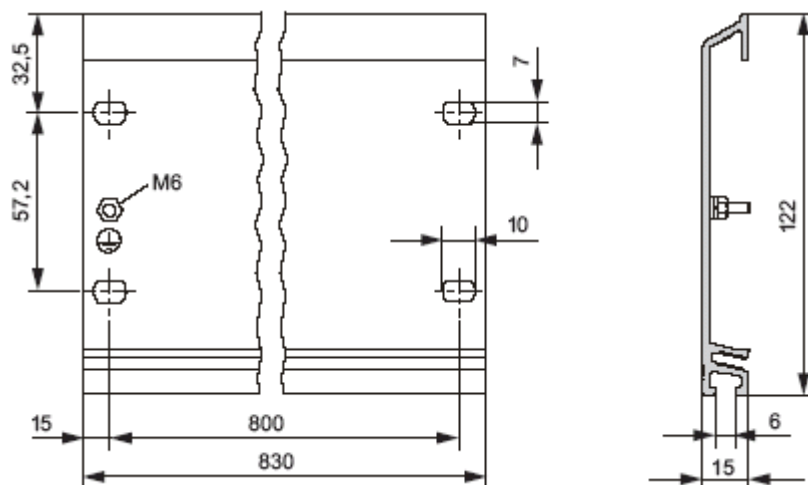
Габаритный чертеж профильной шины стандартной ширины 830 мм.
